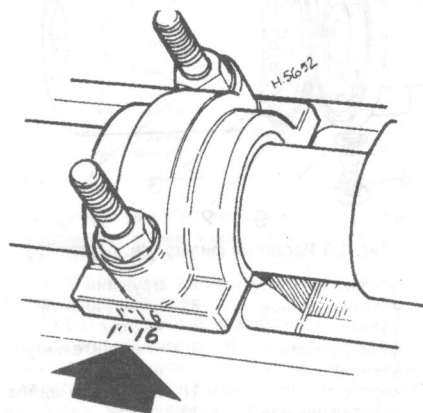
Установочные метки подшипника распредвала (см. раздел 13)
